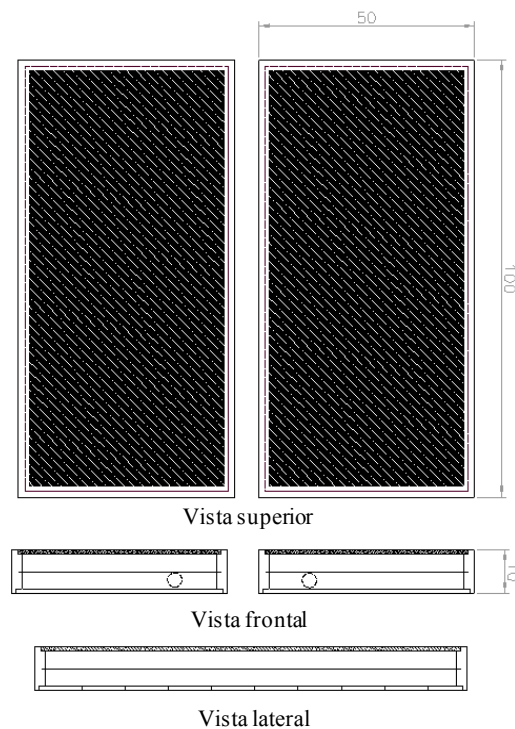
esquema (dimensões em cm) de construção dos painéis, com o revestimento isolante e a cobertura de vidro
